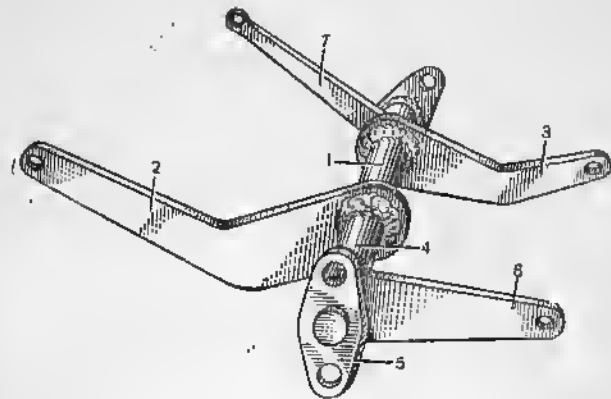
Переходной валок бортового фрикциона и тормоза в сборе; 1 — переходной валок бортового фрикциона; 2 и 3 — рычаги бортового фрикциона; 4 — переходной валок тормоза; 5 — фланец; 6 и 7 — рычаги тормоза
